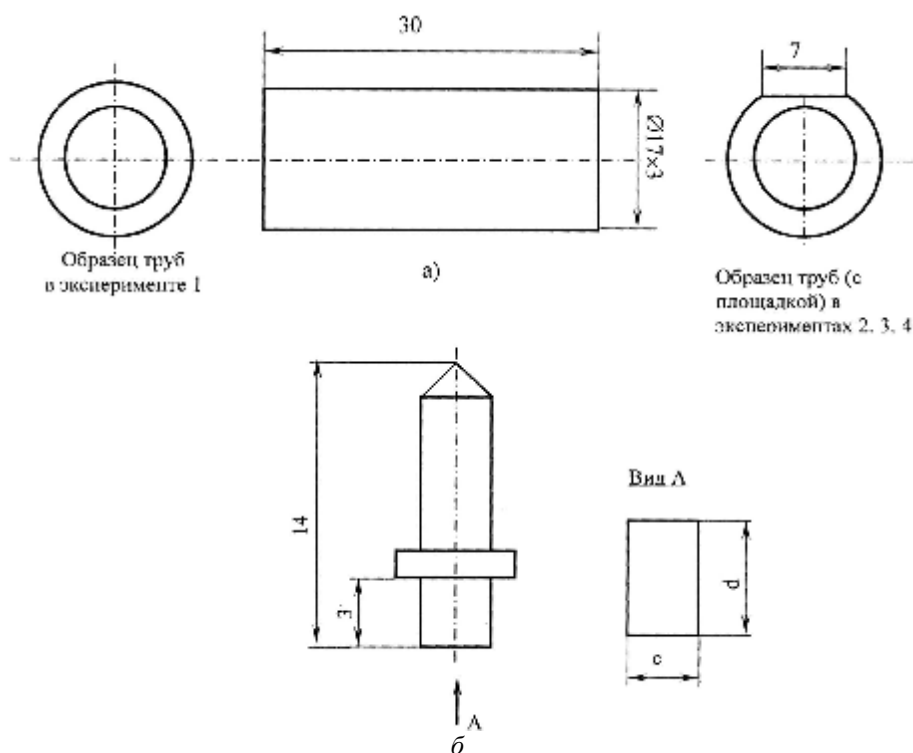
Образцы для испытаний: трубчатый образец (а); контрольный образец (палец) (б)
